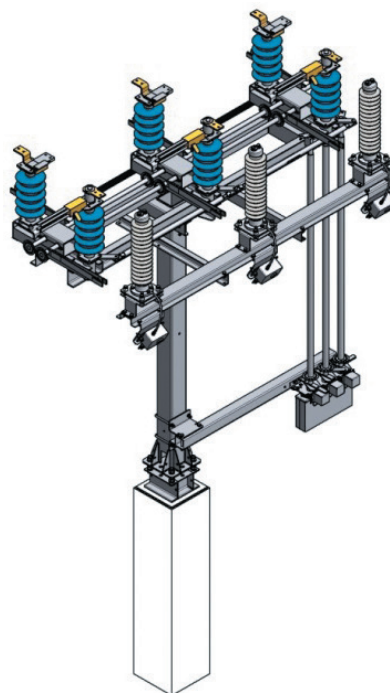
Общий вид блока разъединителя типа РГПЗ-СЭЩ-35 с установленными ОПН-РК-35 и счетчиками СИТ-1
